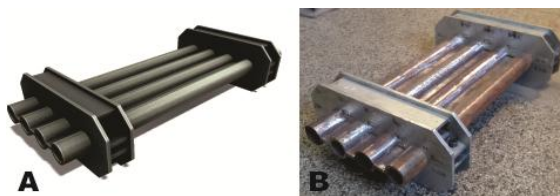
Em (A) projeto do sistema de alinhamento de tubos e em (B) seção de parede pronta para a soldagem de união entre tubo e membrana
